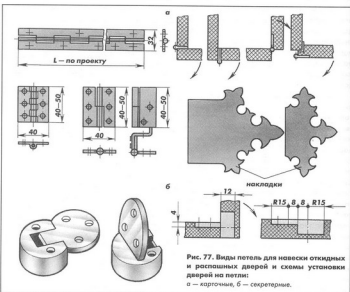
Виды петель для навески откидных и распашных дверей и схемы установки дверей на петли:
